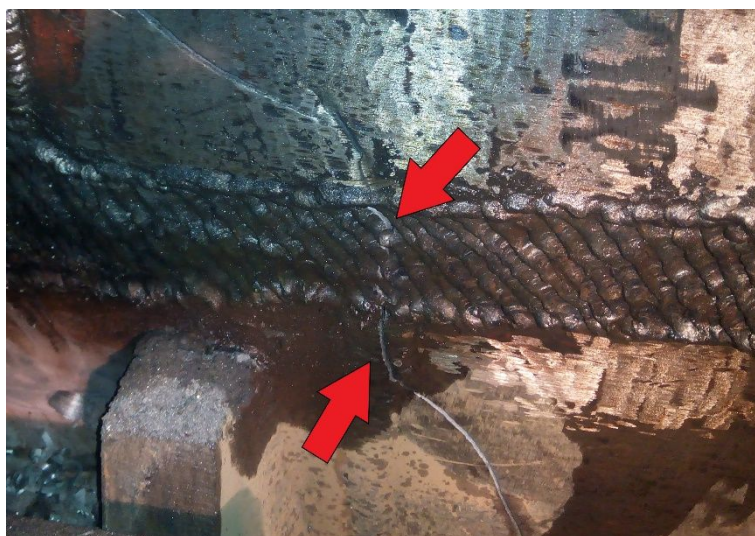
Трещина в сварном соединении стального корпуса конвертера
